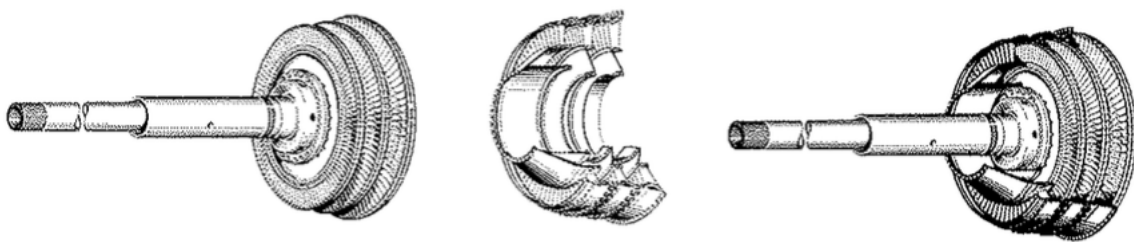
Rotor (1), Estator (2) e montagem (3) de uma turbina axial. [4]
